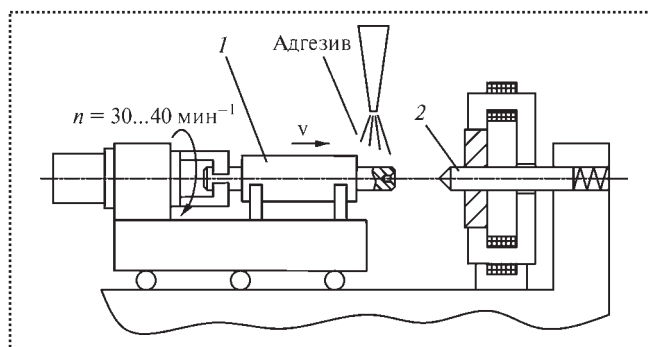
Схема сборочной установки с горизонтальной компоновкой
